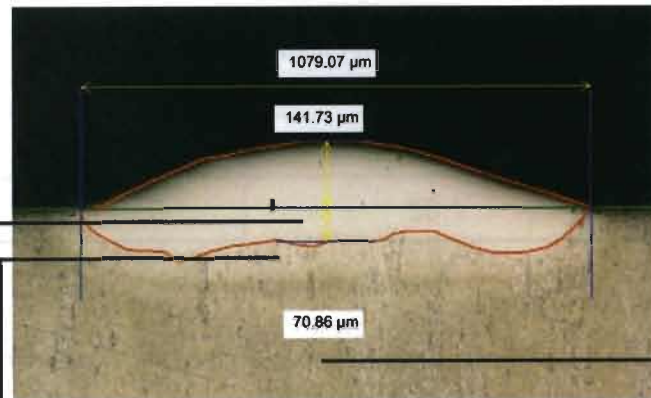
14 Cordón de soldadura #2 visto a 5X
